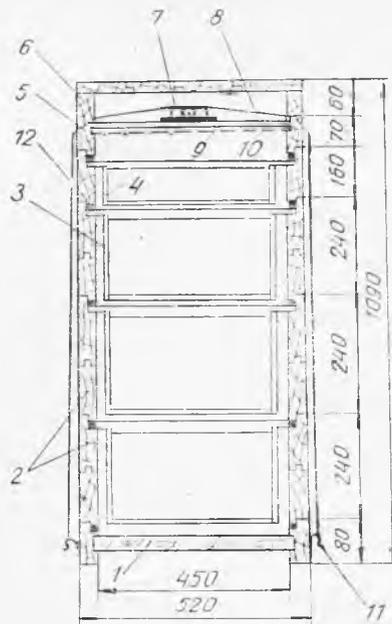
Многокорпусный кочевой улей с магазином в разрезе: 1 — дно; 2 — корпус; 3 — рамки; 4 — магазинные рамки; 5 — кочевая рамка с сеткой; 6 — крышка; 7 — валиковый скреп; 8 — проволочные тяги; 9 — дощечка со скрепом; 10 — металлическая сетка; 11 — крючок; 12 — резиновая трубка.
